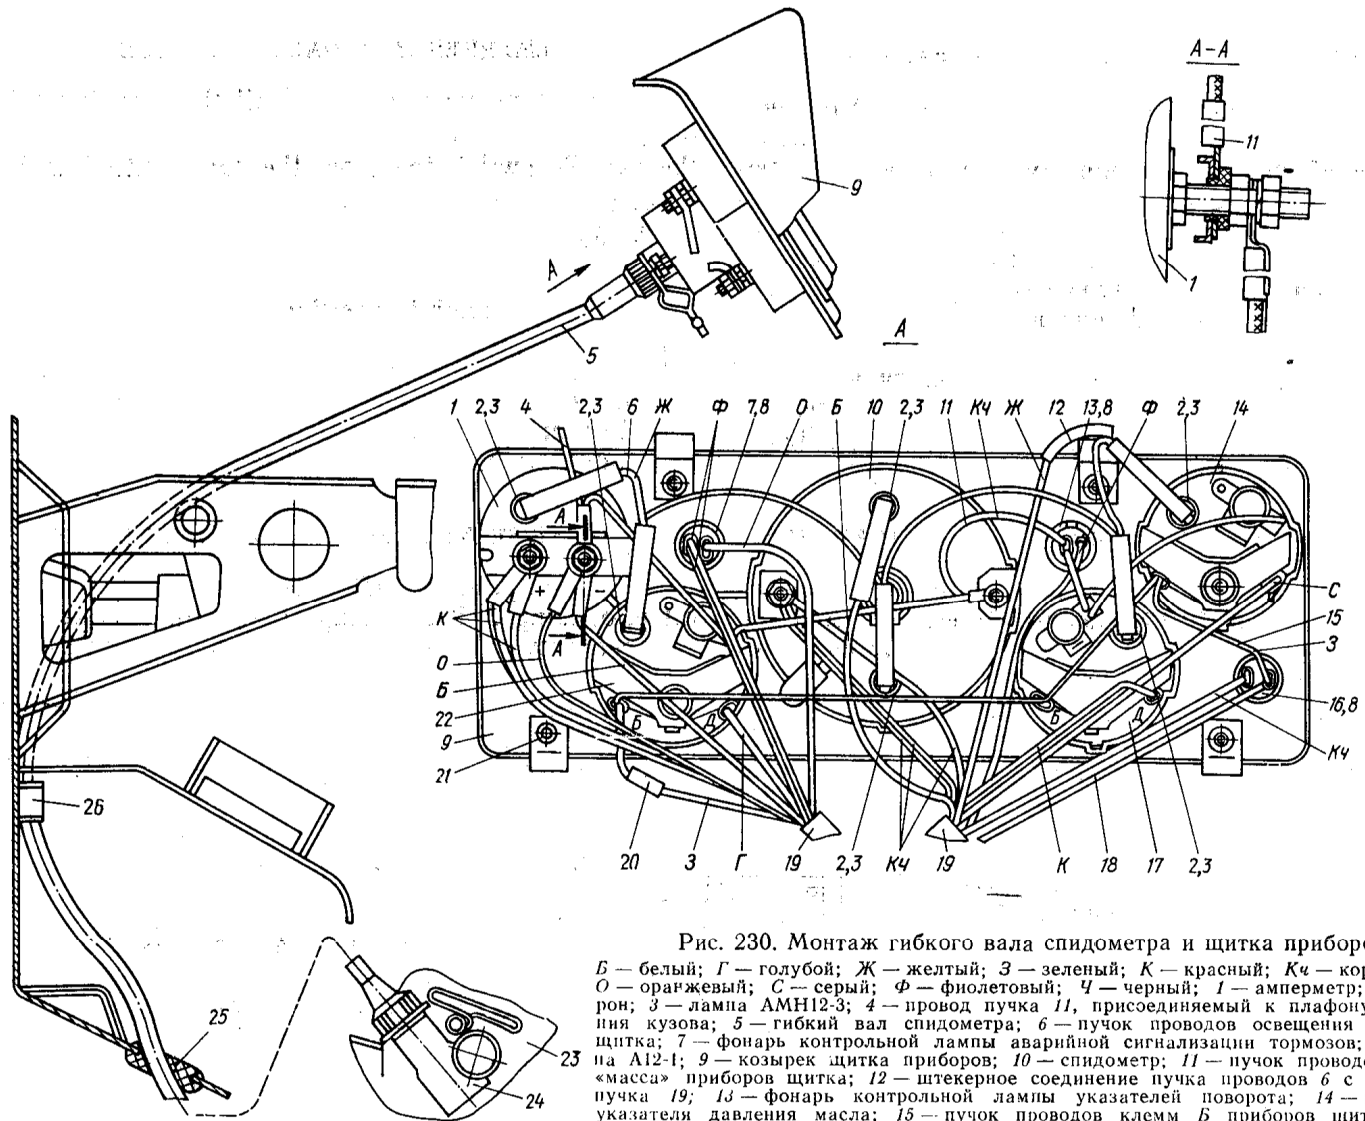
Монтаж гибкого вала спидометра и щитка приборов:
